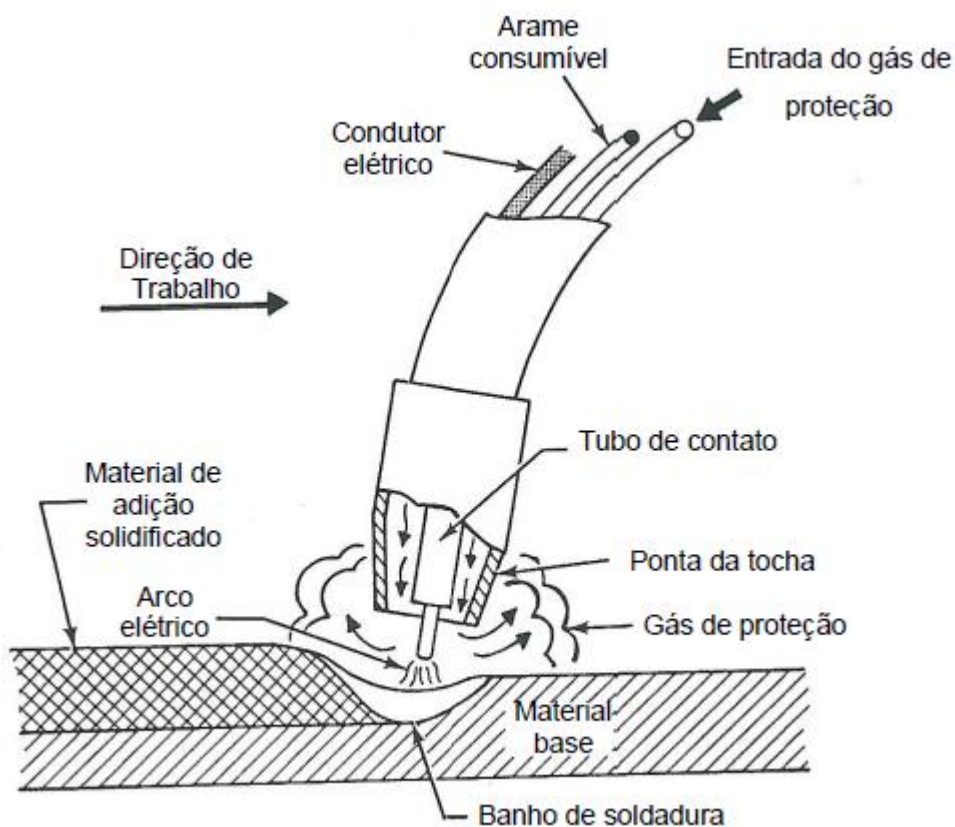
Processo de soldadura GMAW (MIG/MAG) (fonte: migweldhowto).
